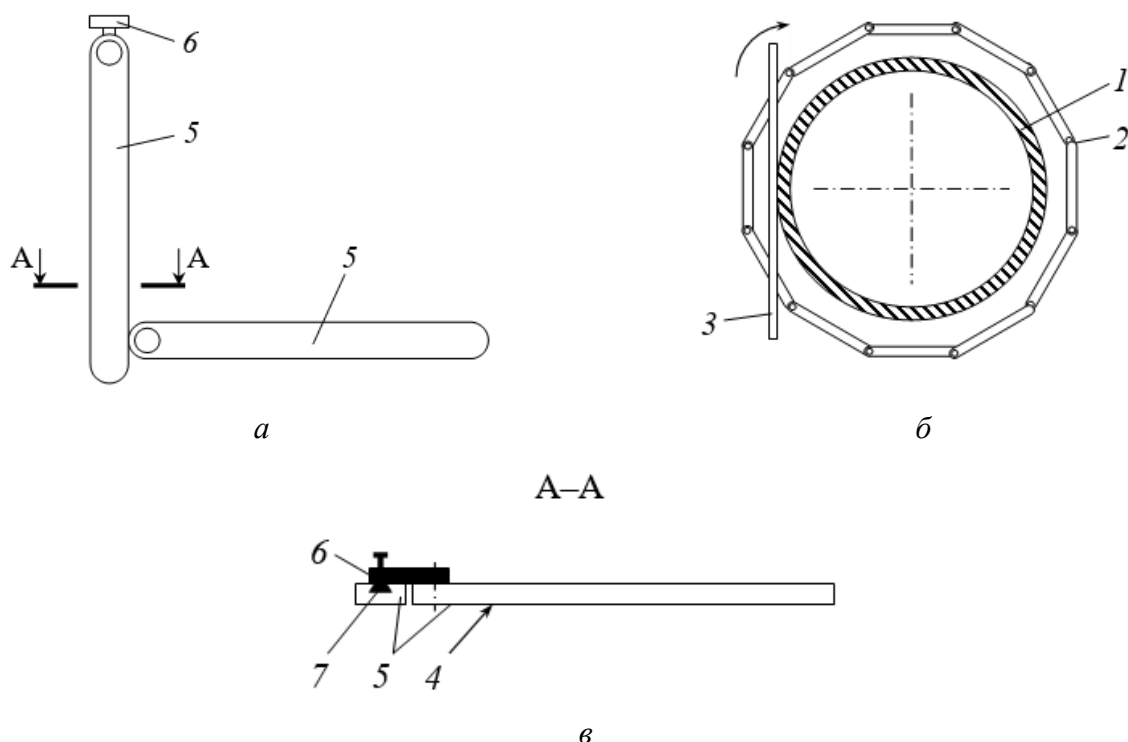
Конструкція пристрою для розмічання скошеного місця розрізання циліндричного об'єкта до пат. України 157736 U [4]: *а* – схема роботи пропонованого пристрою; *б* – схема розташування сусідніх поздовжніх елементів рамного елемента; *в* – розріз за А–А на рис. 1, *б* (пояснення в тексті)
